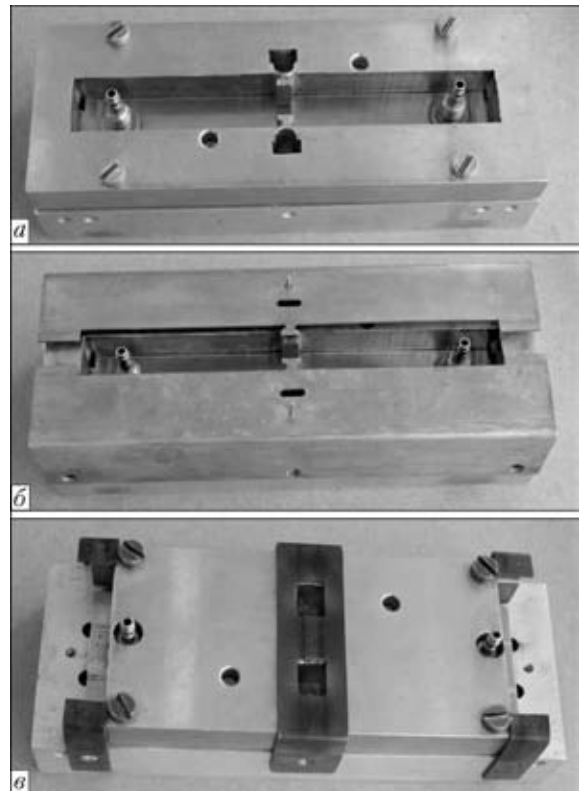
Сборочно-сварочное приспособление для электронно-лучевой сварки измерительной камеры ($\times 1,67$): а — сборка без защитных экранов; б — сборка с защитными экранами для выполнения нахлесточных швов соответственно вдоль длинной и короткой (в) сторон
